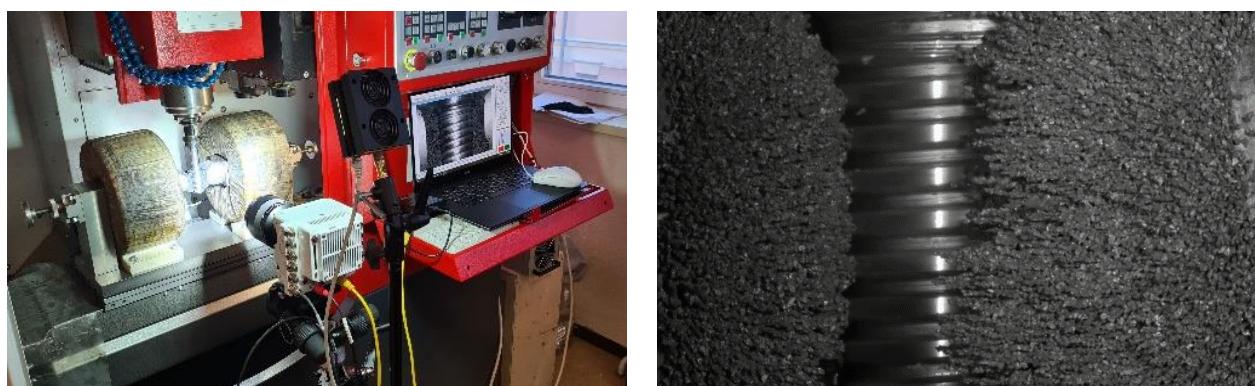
Процесс магнитно-абразивной обработки наружной резьбовой поверхности буровой штанги
